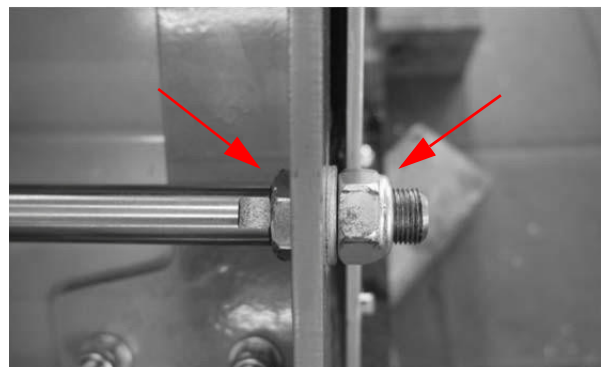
Bevestiging voor hydraulische cilinder, rechts
